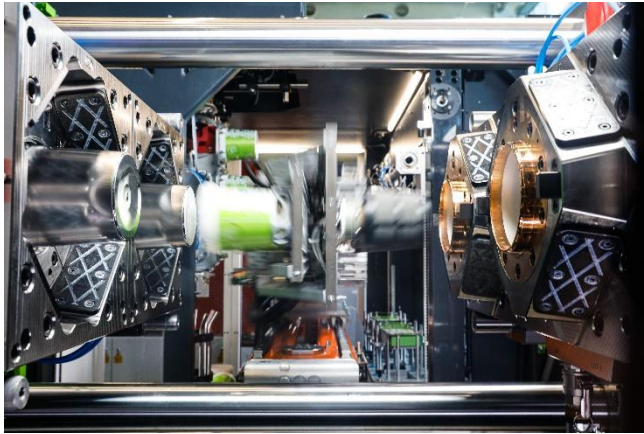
Das Werkzeug für den 1,3 L Eimer auf einer vollelektrischen e-motion 765/280 T.
